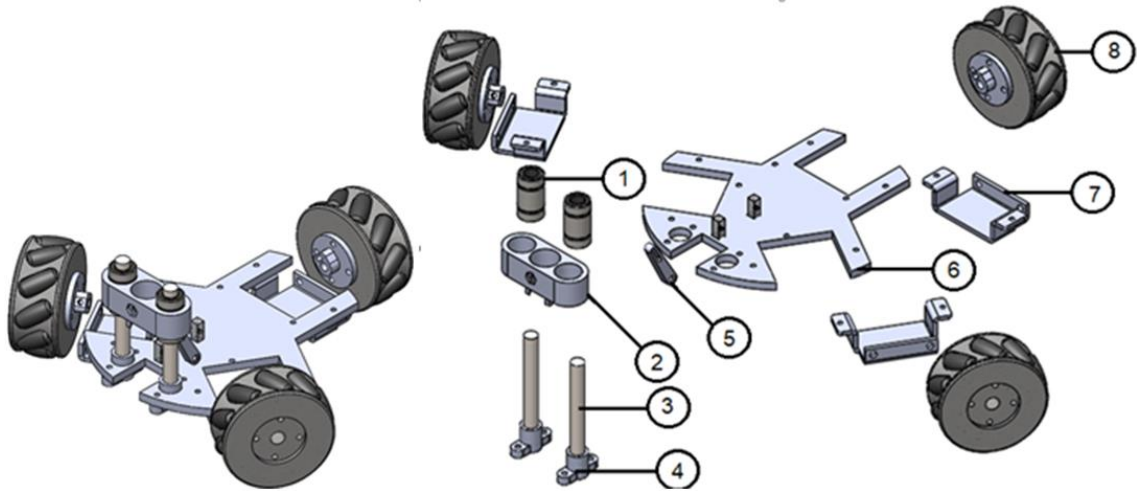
Vista isométrica y explosionada respectivamente del diseño mecánico
